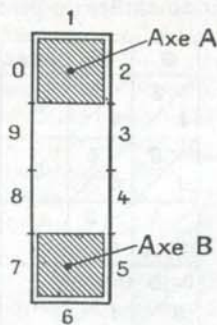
Section droite d'une réglette, dans la machine de M. Marcou.
